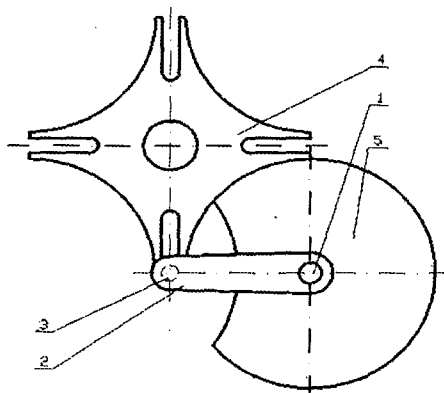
Krokovací mechanizmus s valcovou vačkou [20]
